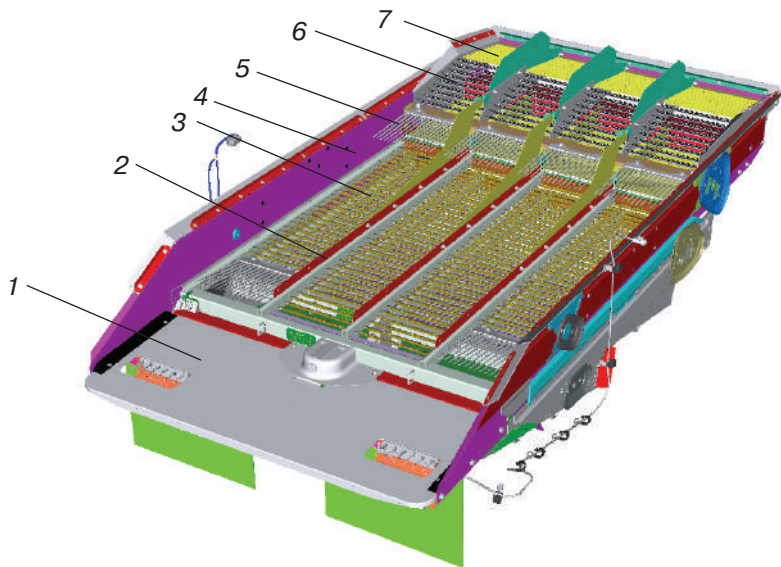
Верхній решітний стан із попереднім очищенням комбайна «John Deere»: 1 — подовжувач; 2 — подовжні ребра; 3 — верхнє решето; 4 — борт; 5 — решітка; 6 — похила жалюзійна надставка (решето попереднього очищення); 7 — стрясна дошка
